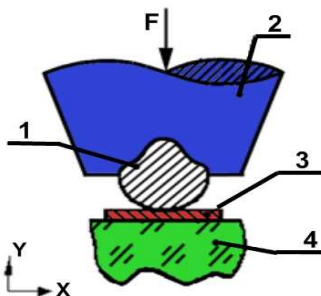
Схема УЗ сварки: 1 – проволока; 2 – сварочный инструмент; 3 – контактная площадка; 4 – кристалл
